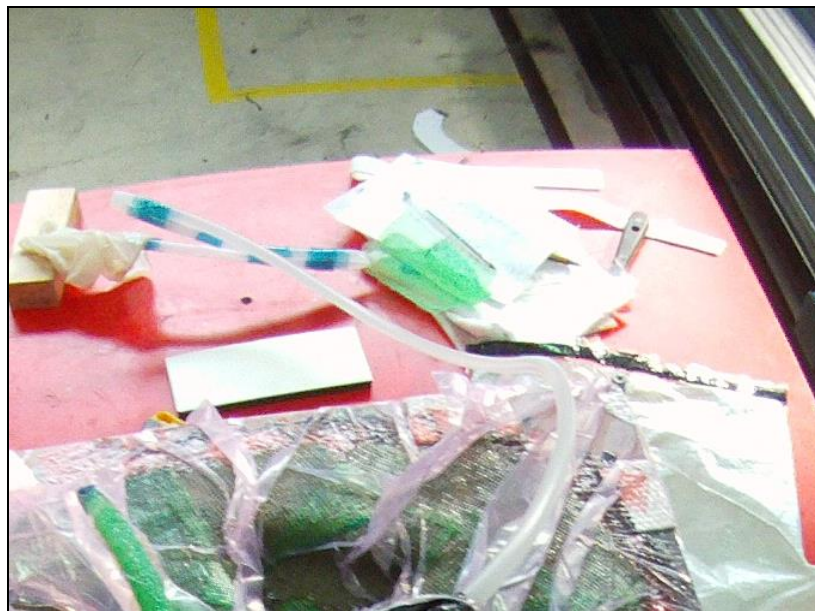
Detalle del cierre del tubo de aspiración mediante una 'Z'
